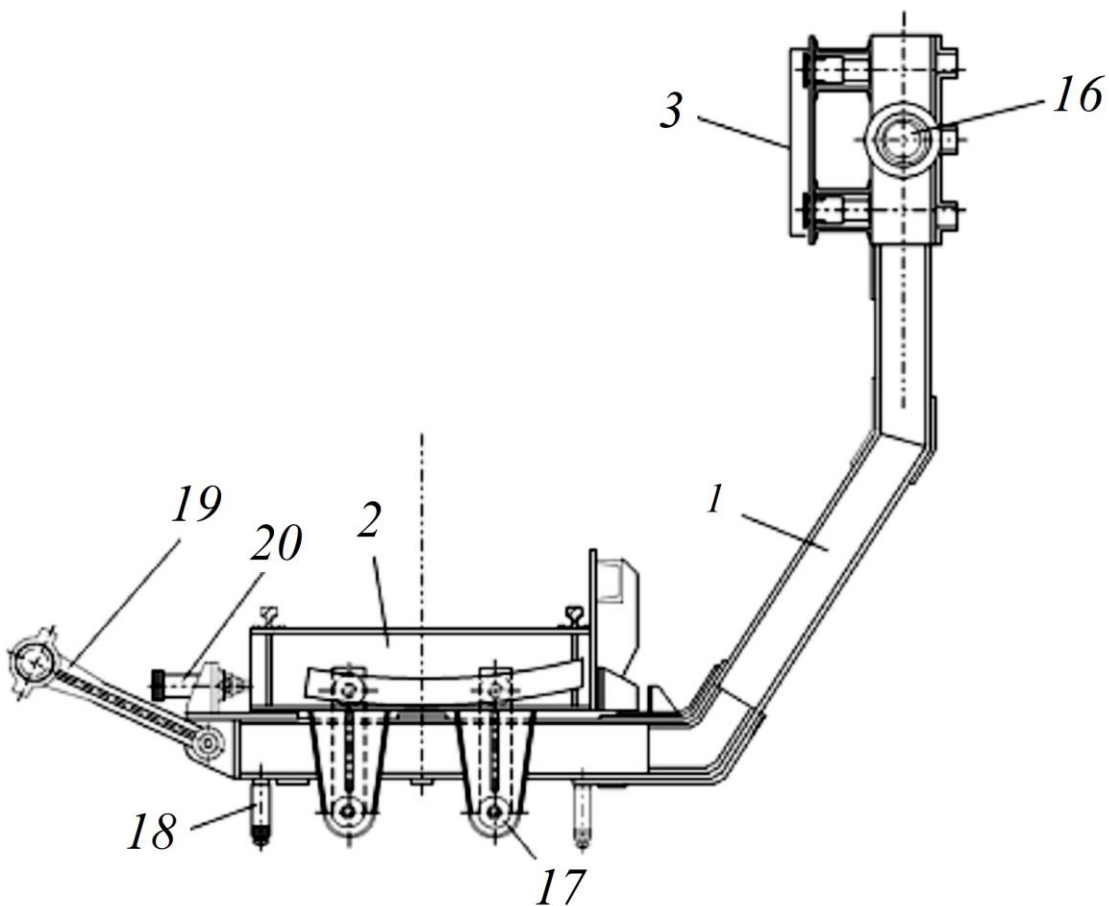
Конструкція люльки роторного вагоноперекидача
